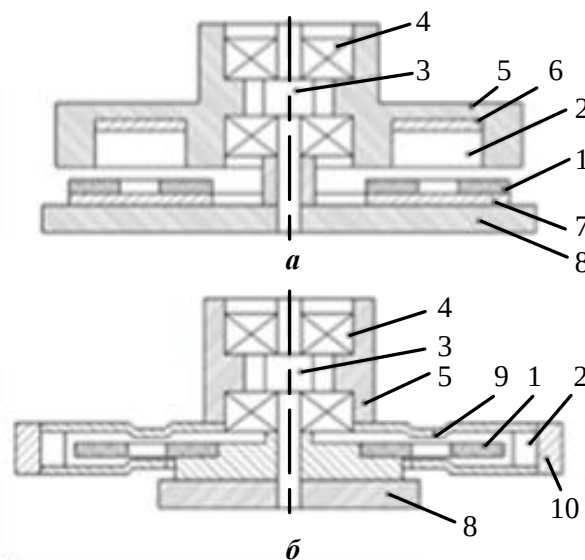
Конструкция дискового привода жесткого диска компьютера: 1 – катушки статора; 2 – ВПМ; 3 – вал; 4 – подшипники; 5 – ступица; 6 – ядро ротора; 7 – ядро статора; 8 – основание; 9 – конструкционные изгибы; 10 – немагнитное кольцо
